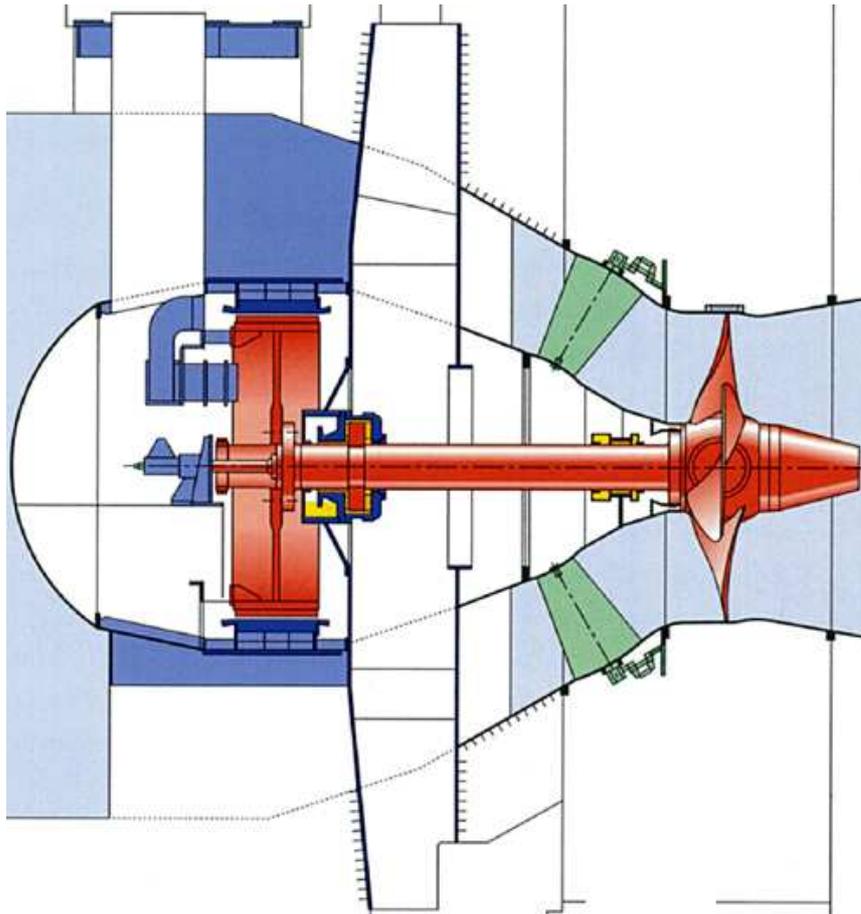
Corte esquemático de uma turbina de eixo horizontal tipo Bulbo.
